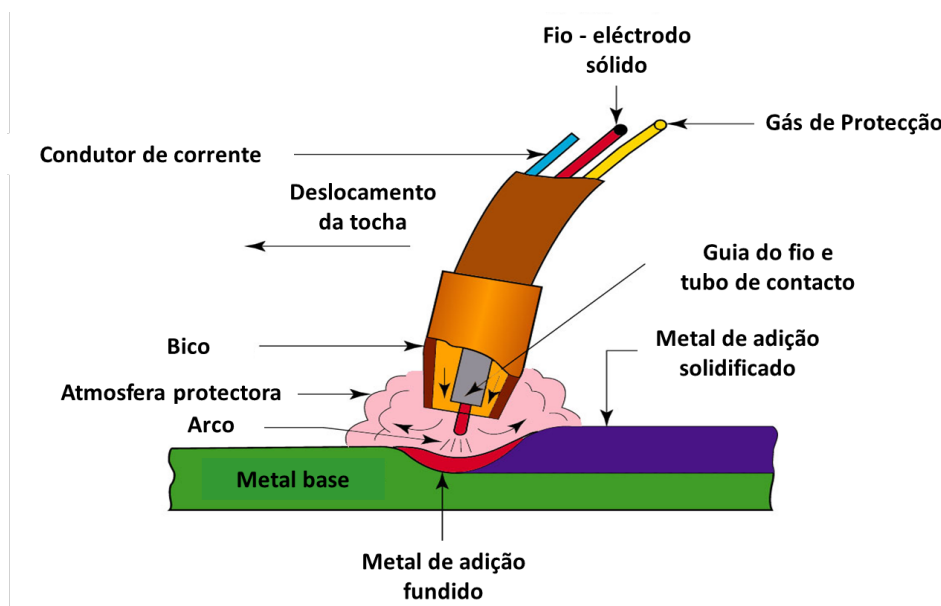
Processo de soldadura MAG (Retirado de: Silva, 2016)
